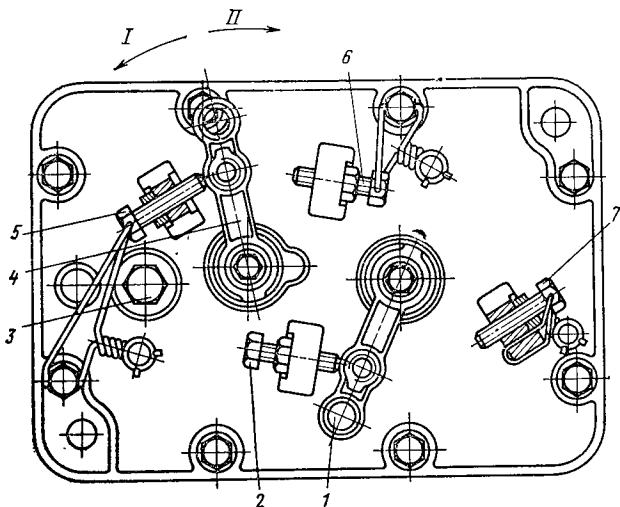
Крышка регулятора с рычагами подачи топлива и останова двигателя: I — работа; II — выключено; 1 — рычаг управления регулятором; 2 — болт ограничения минимальной частоты вращения; 3 — пробка заливного отверстия; 4 — рычаг останова; 5 — болт регулировки пусковой подачи; 6 — болт регулировки хода рычага останова; 7 — болт ограничения максимальной частоты вращения
